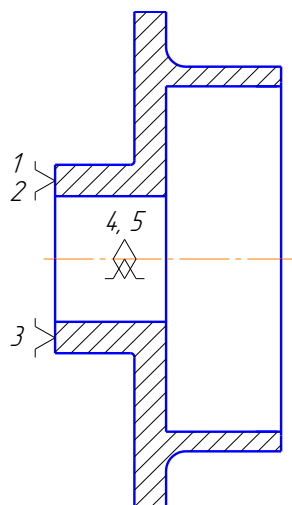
Теоретична схема базування деталі "Корпус"
